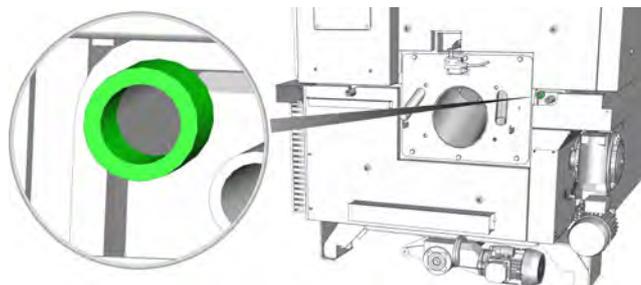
Raccord pour sonde de température de la soupape thermique de la chambre de combustion
